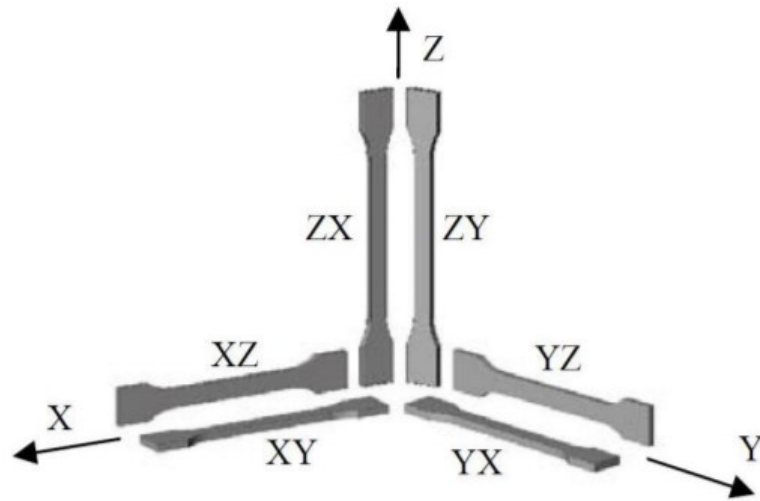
Disposizione dei provini nello spazio in funzione dell'orientazione dell'asse del provino rispetto alla direzione di crescita.
